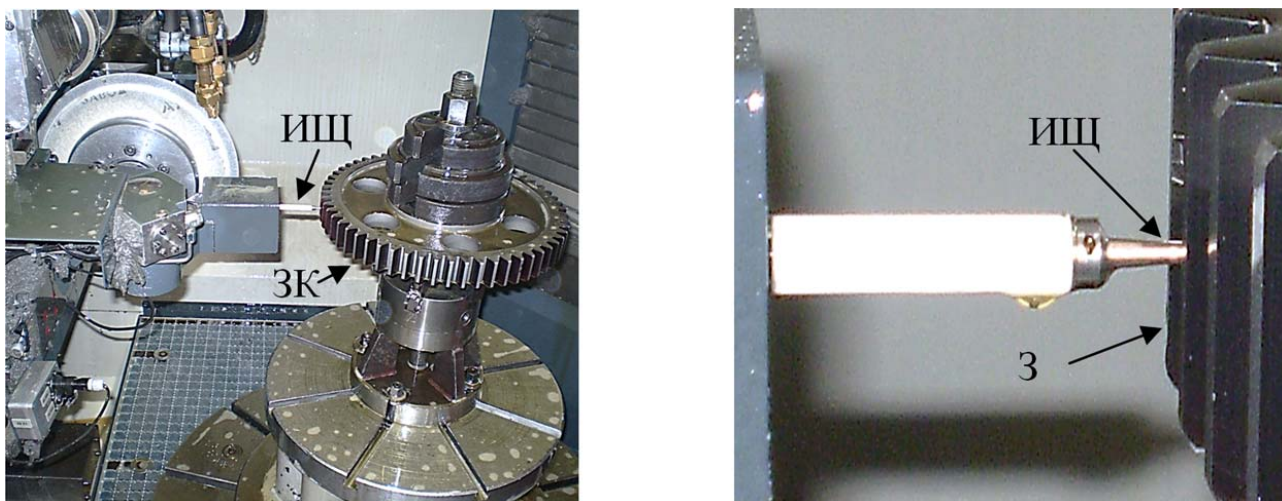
Измерение припуска и параметров обработки на станке HOFLER RAPID 1250: ИЩ – измерительный щуп компании Renishaw; ЗК – обрабатываемое зубчатое колесо: общий вид (слева) и зона измерения (справа)
